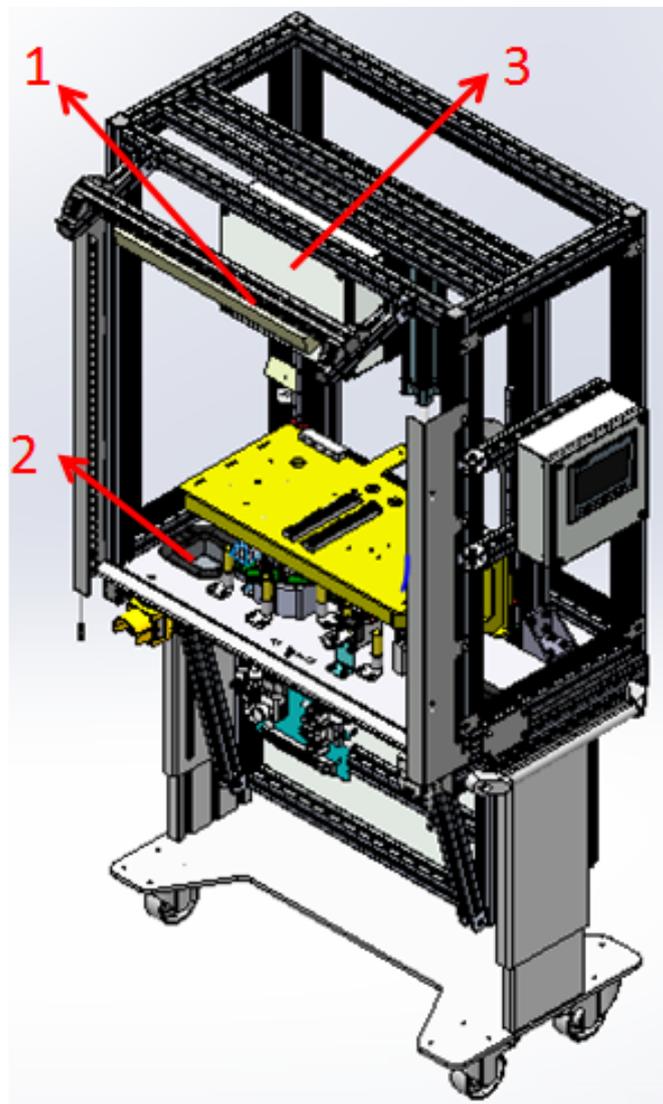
Diseño final máquina/ 1; Luminaria /2; Cuba /3; Sinóptico
